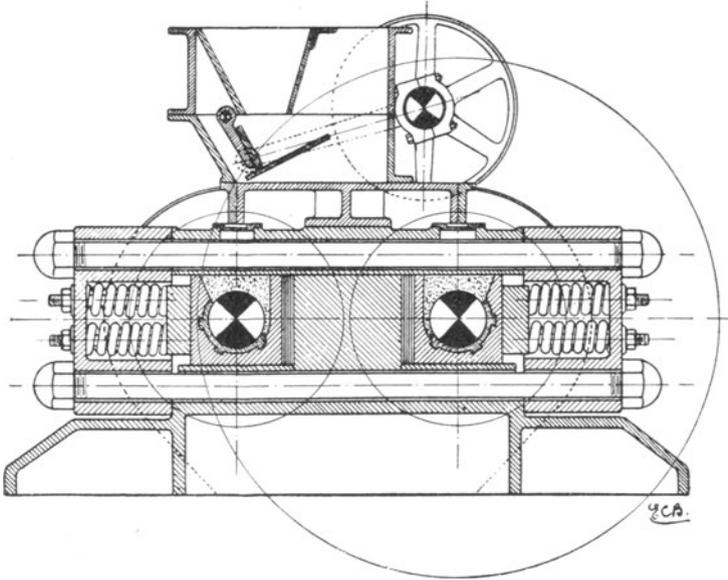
Walzwerk mit ausgeglichenen Walzen von Sturtevant.
